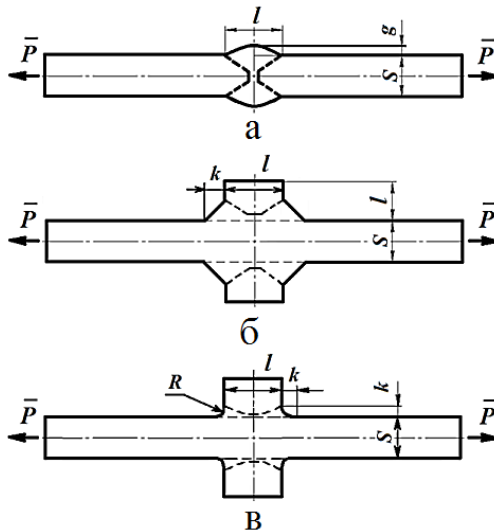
Геометричні форми зварних з'єднань:– стикове (а) та таврові з'єднання (б, в)
